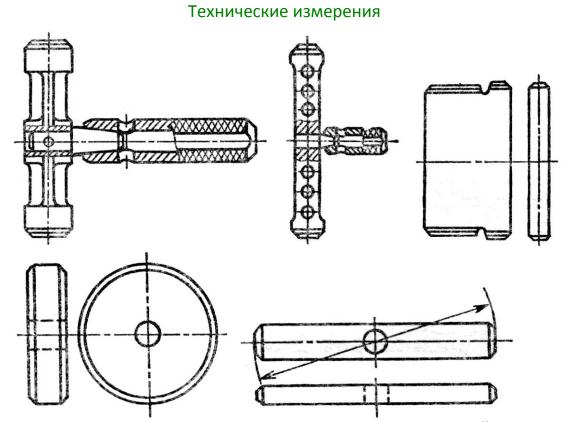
Основные типы калибров-пробок для контроля отверстий
